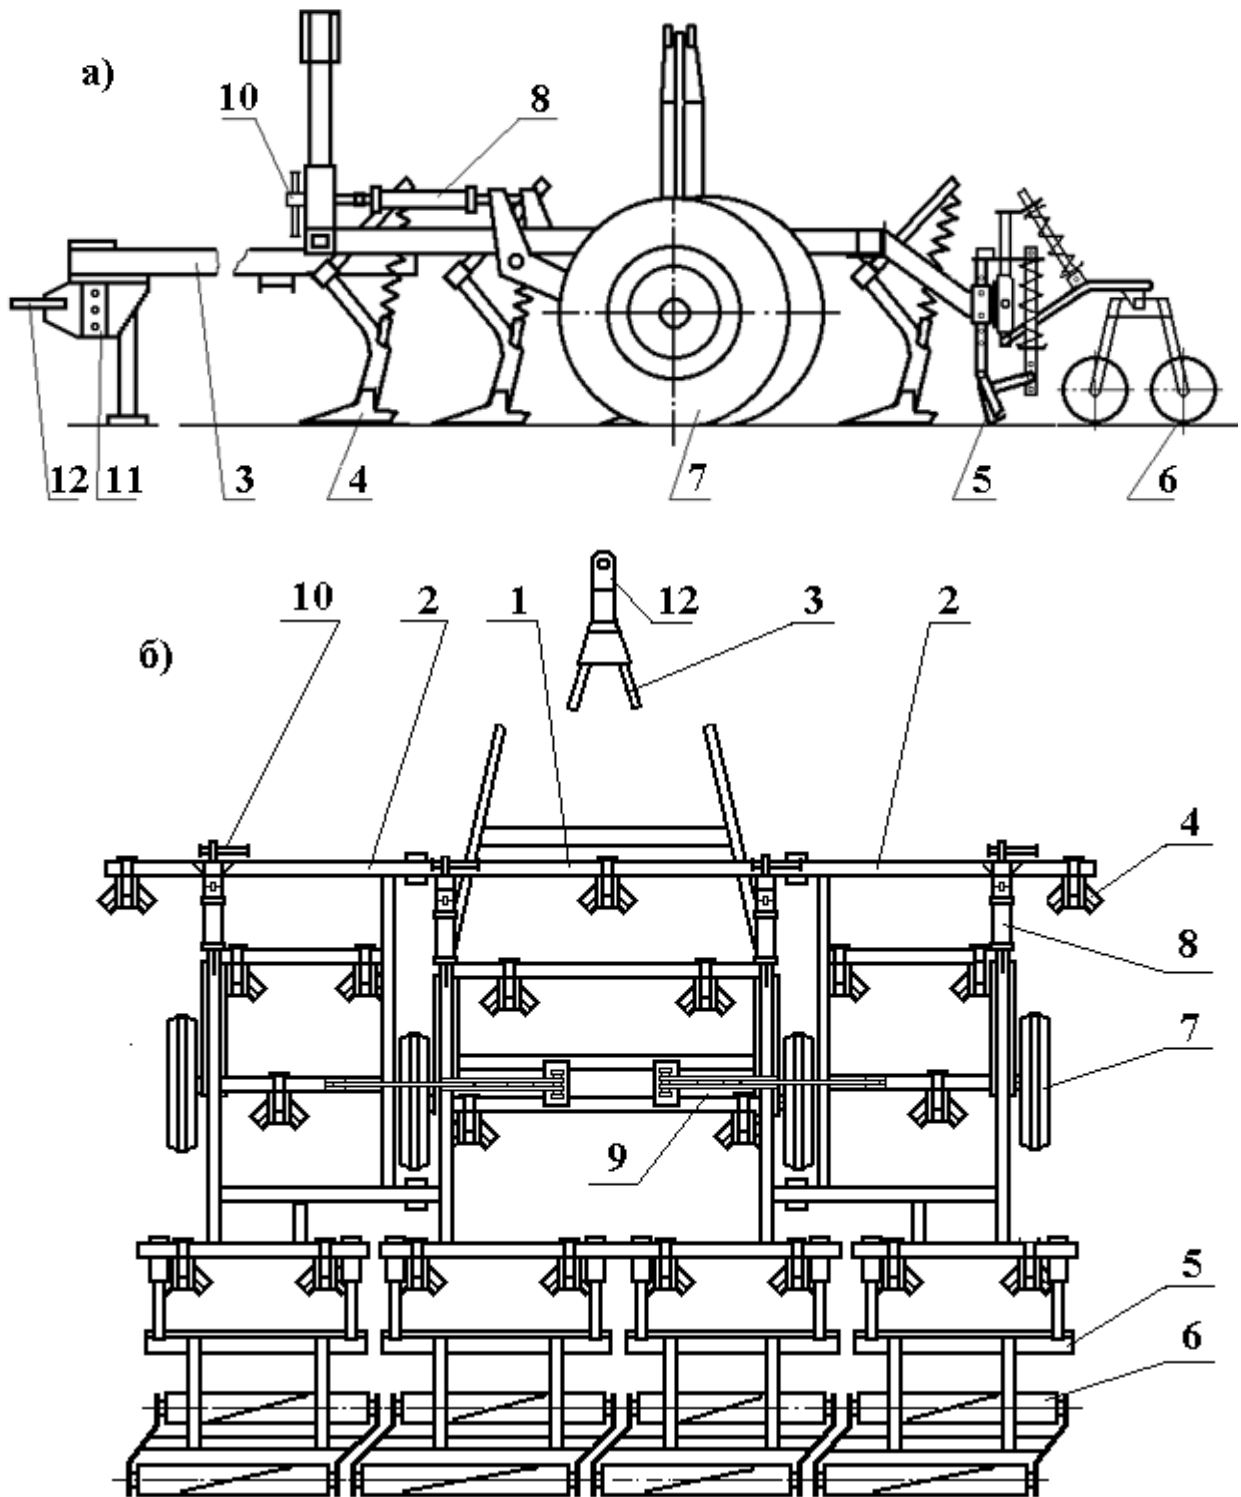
Культиватор КПО-6: а) вид сбоку б) вид сверху
